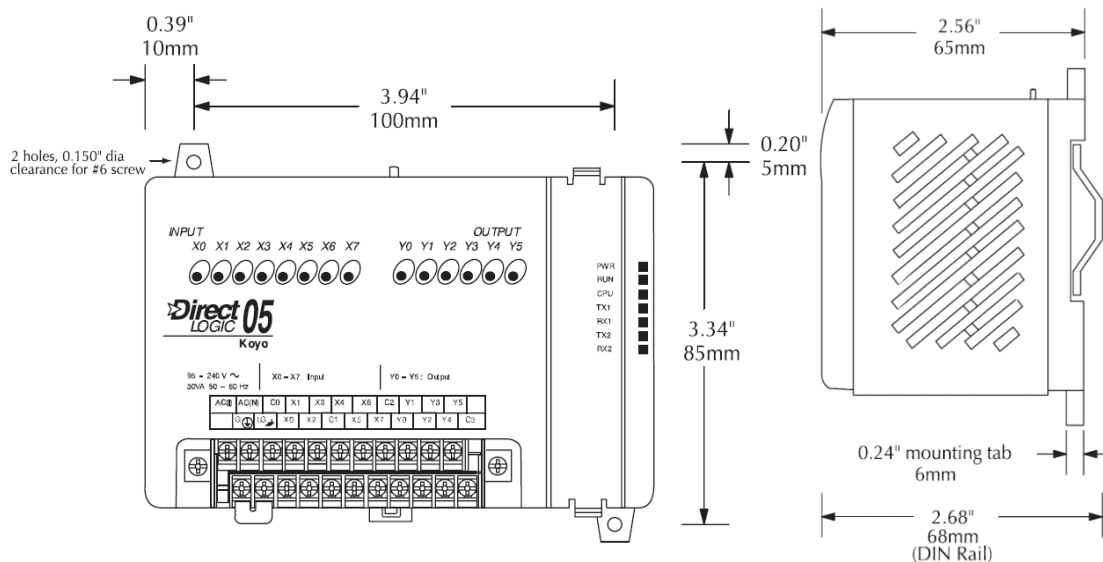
Dimensiones para montaje del PLC DL05⁶⁷
